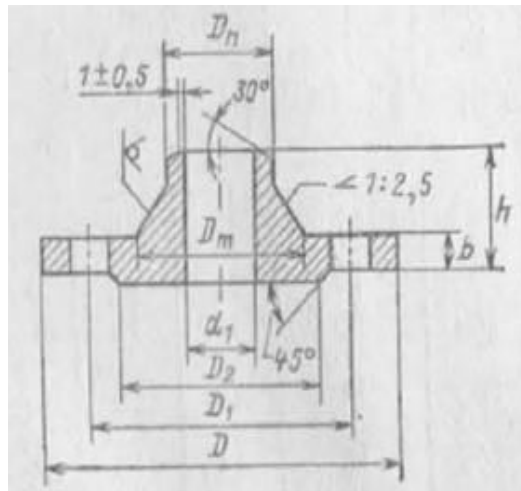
Фланец приварной встык с шейкой и соединительным выступом
